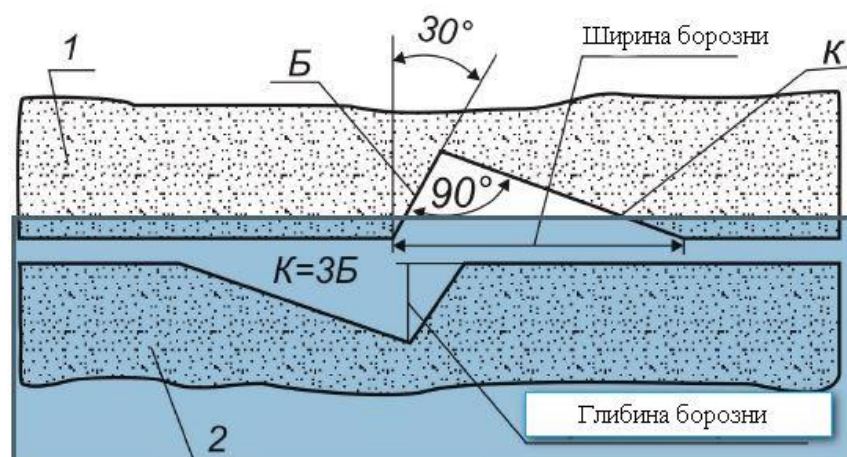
Поперечний переріз борозенки: 1 – верхній камінь; 2 – нижній камінь, Б – крута стінка, К – полого стінка
